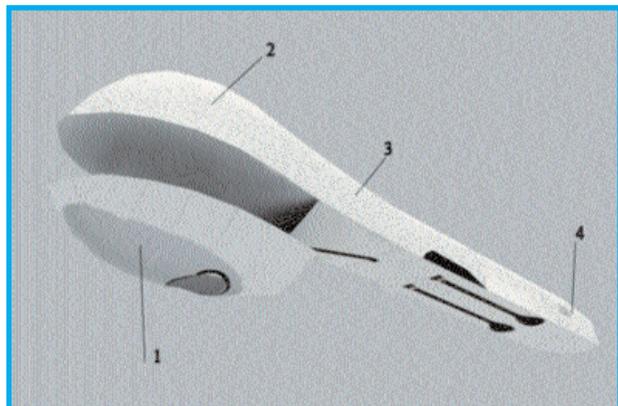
Компоновка фюзеляжа: 1 — контейнер для фотовидеокамеры; 2 — контейнер для аппаратуры дистанционного управления; 3 — место крепления консолей крыла; 4 — задняя часть модели
